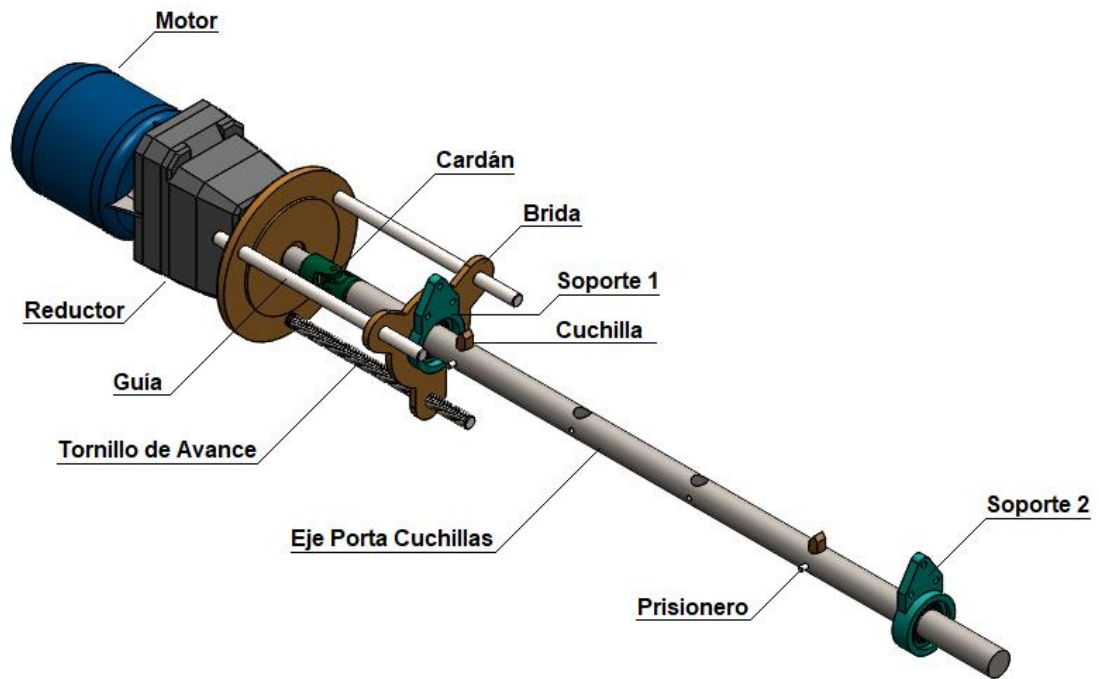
Maquina Mandrinadora. (Modelamiento SolidWorks)
